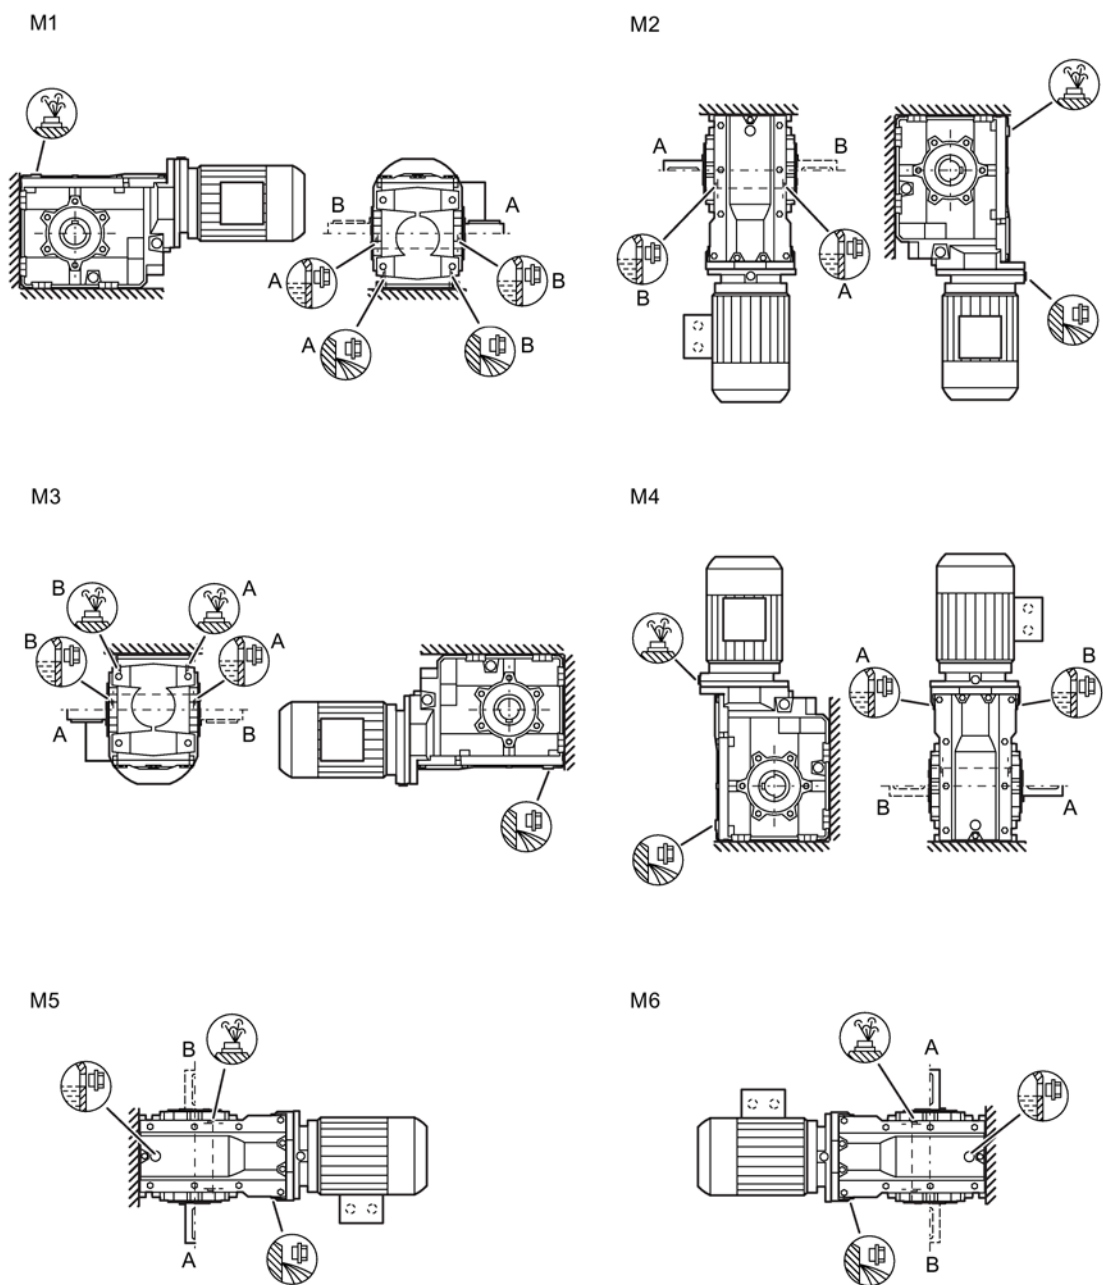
Монтажные положения для конического редуктора В. в исполнении на лапах, типоразмеры 39–49
